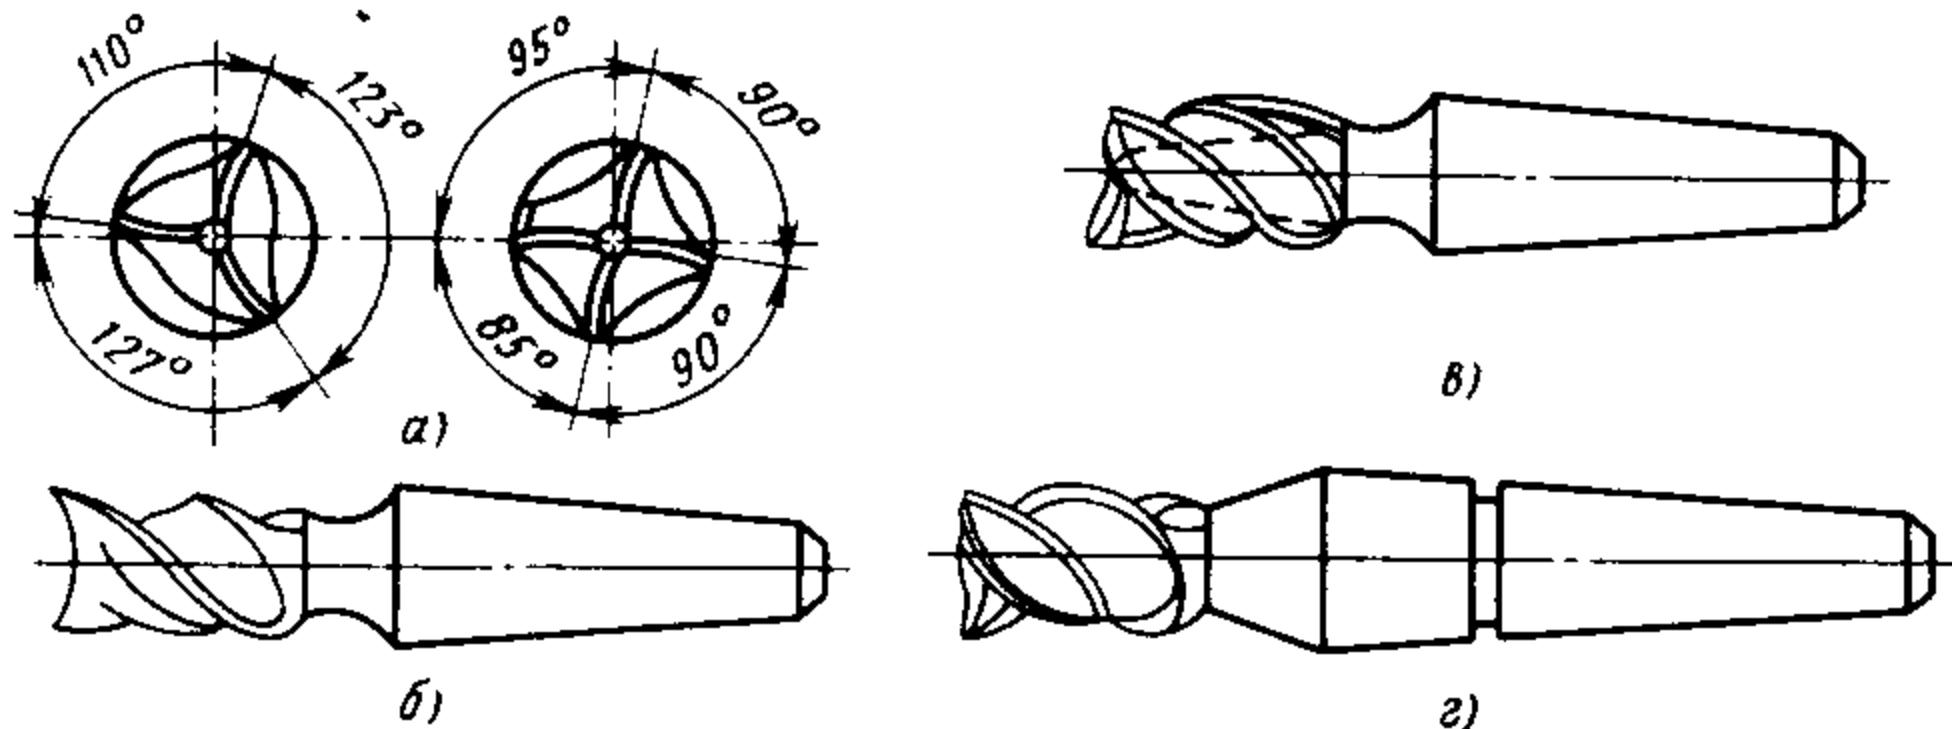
Концевые фрезы для станков с ЧПУ:
